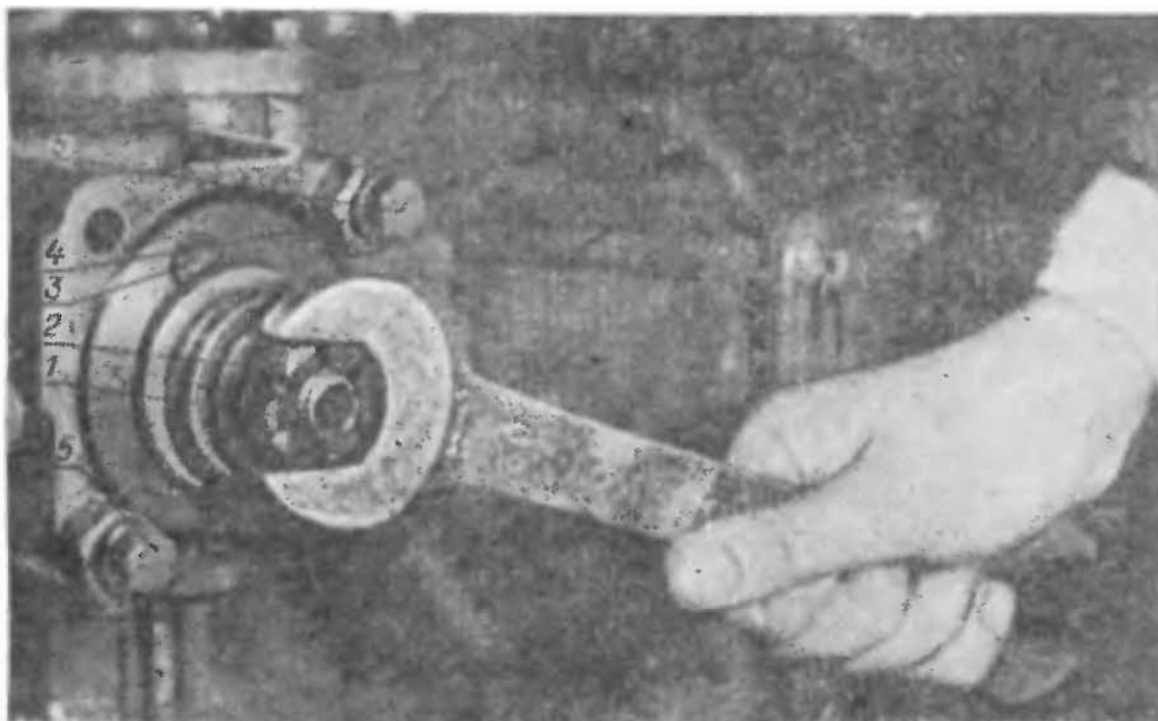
Установка распределителя и затяжка сферической гайки червяка:
